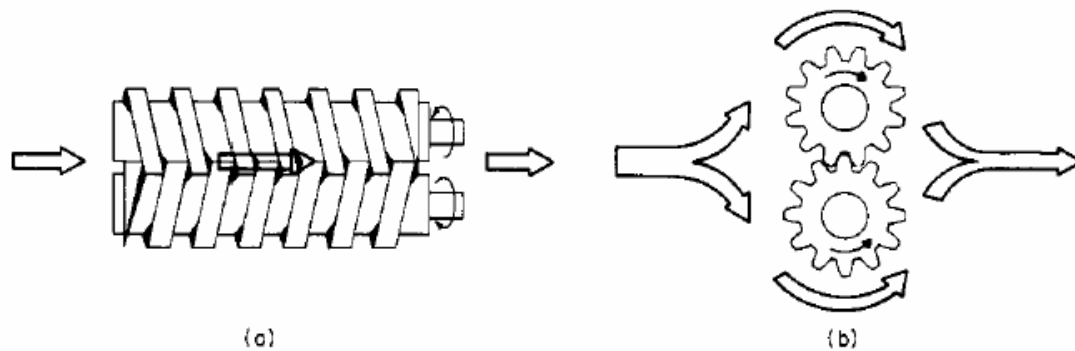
Diagramas de una bomba de tornillos y de engranajes, mostrando movimiento axial (a) y circular (b) del fluido
